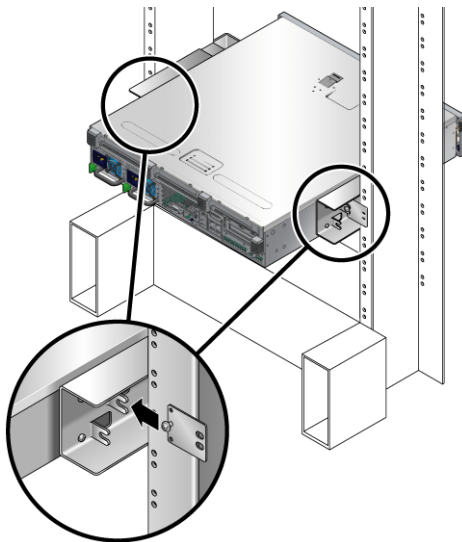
Installation de la plaque arrière sur le support latéral
